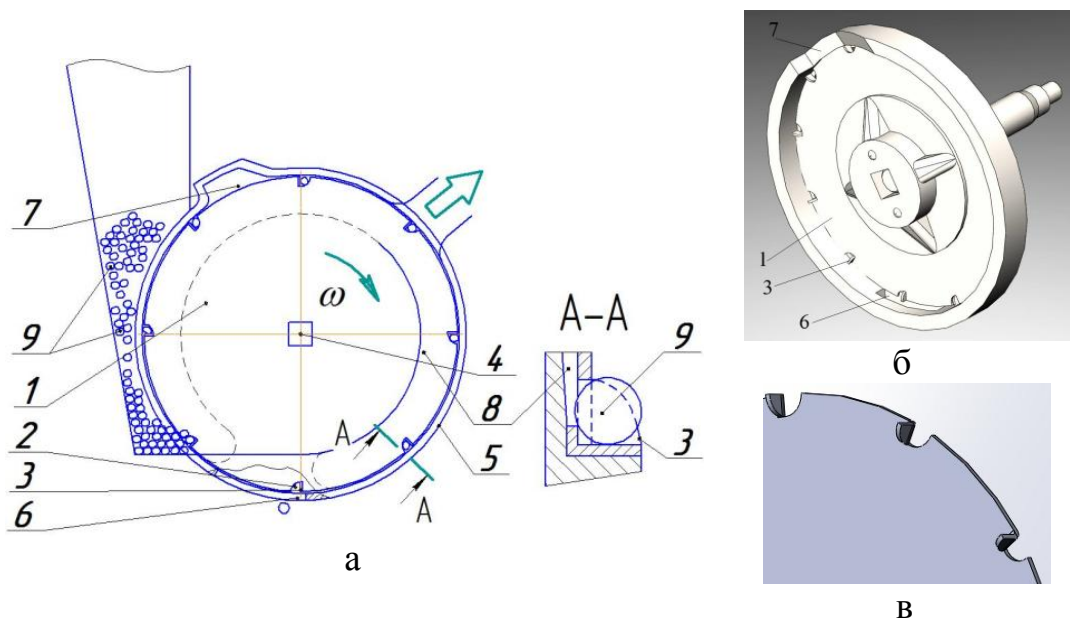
Запропонований пневмомеханічний висівний апарат: 1 – висівний диск; 2 – комірка; 3 – лопатка; 4 – приводний вал; 5 – корпус; 6 – висівне вікно; 7 – пасивний пристрій (порожнина) для видалення зайвого насіння; 8 – вакуумна камера; 9 – насіння; а – схема; б – тривимірна модель висівного апарата; в – тривимірна модель фрагмента висівного диска
